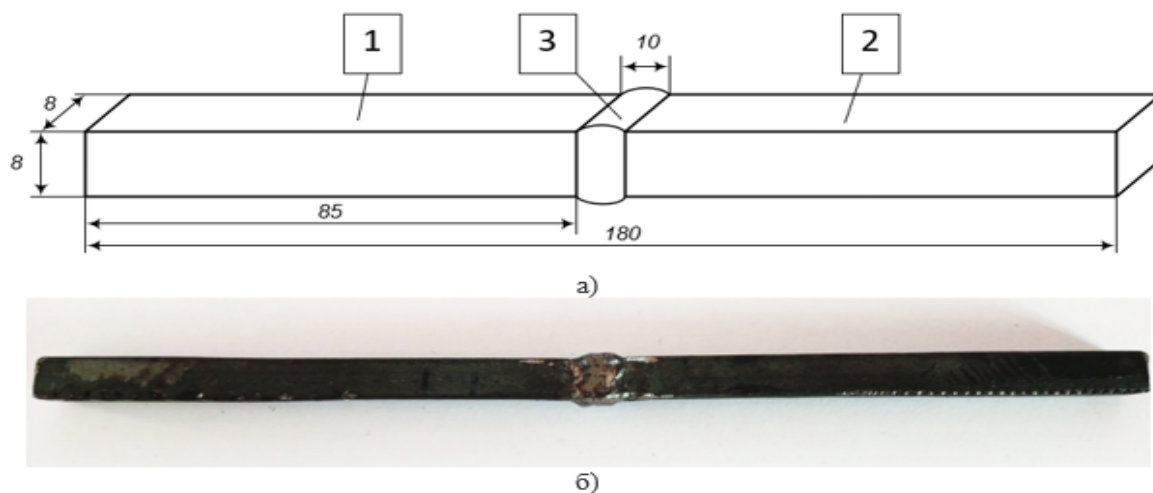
Експериментальний зразок: а) схематичний вигляд експериментального зразка (1, 2 – заготовки з сталюого прутка; 3 – зварний шов); б) загальний вигляд зразка.
